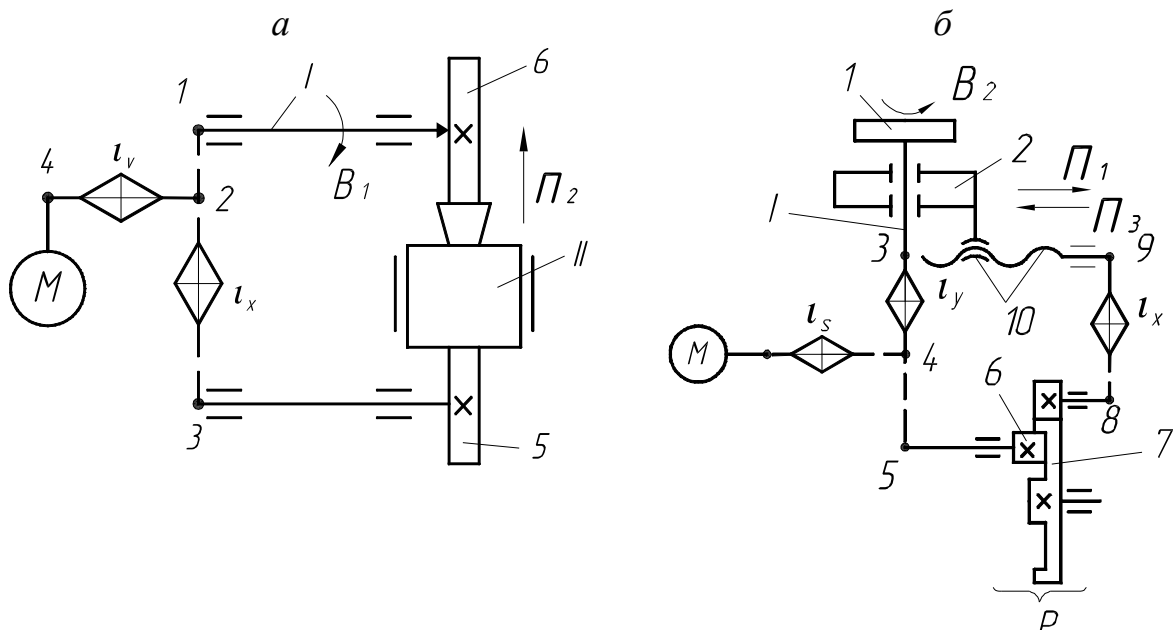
Кинематическая структура со смешанным соединением групп формообразования и деления: а – затыловочного станка; б – зубошлифовального станка
